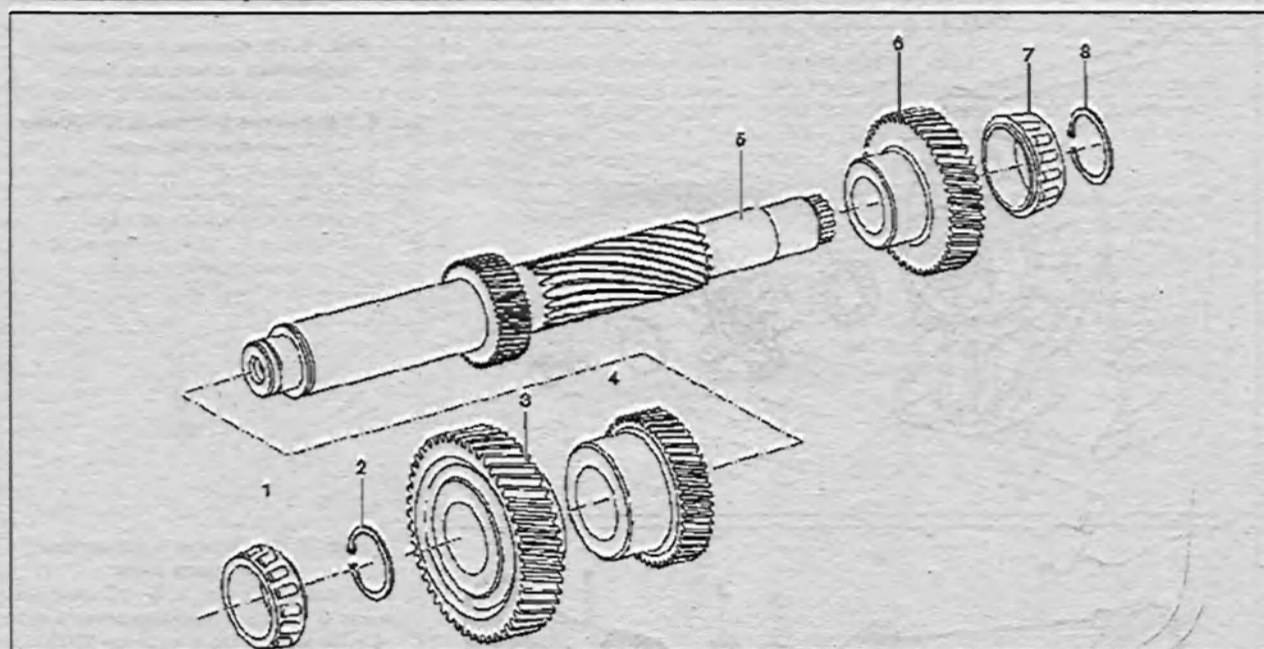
Разборка и сборка промежуточного вала МКПП 711.620/621:
